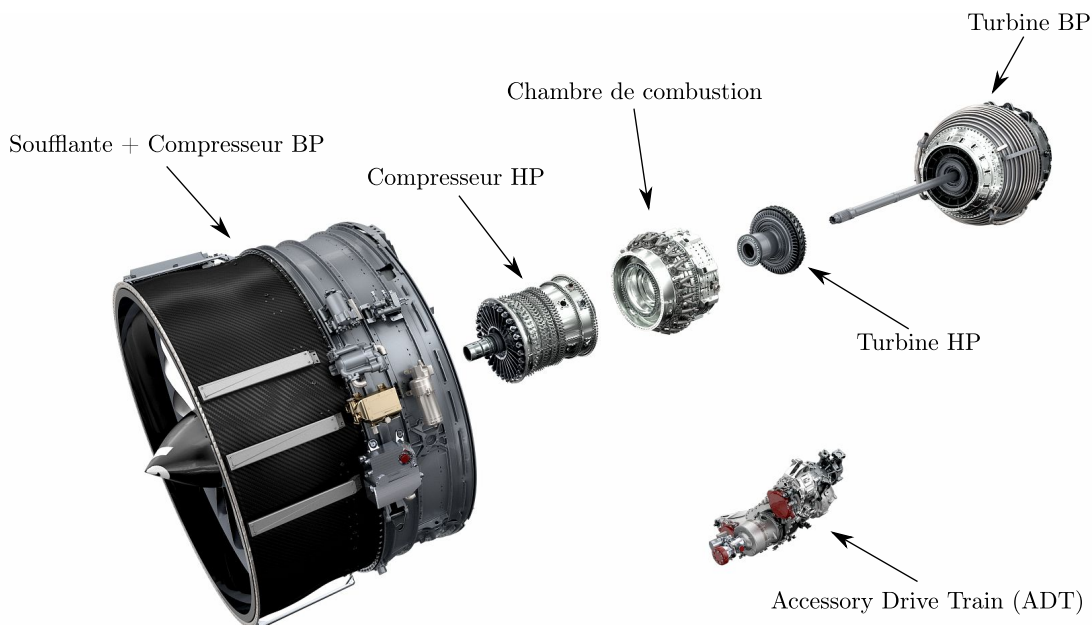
Vue éclatée d'un turboréacteur LEAP-1A
